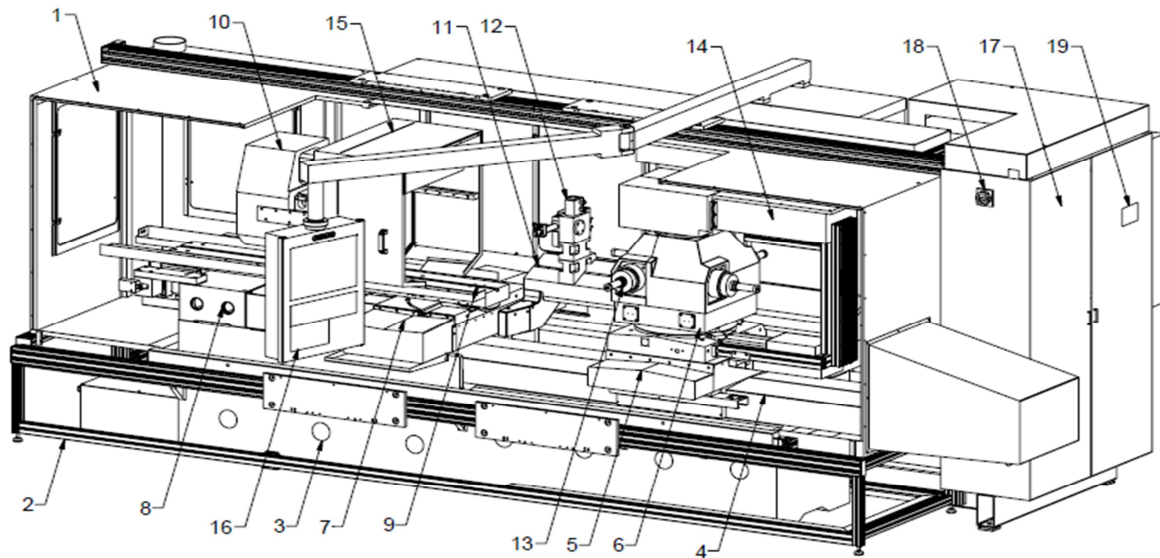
Emplacement des éléments principaux de la vue de face de la machine
